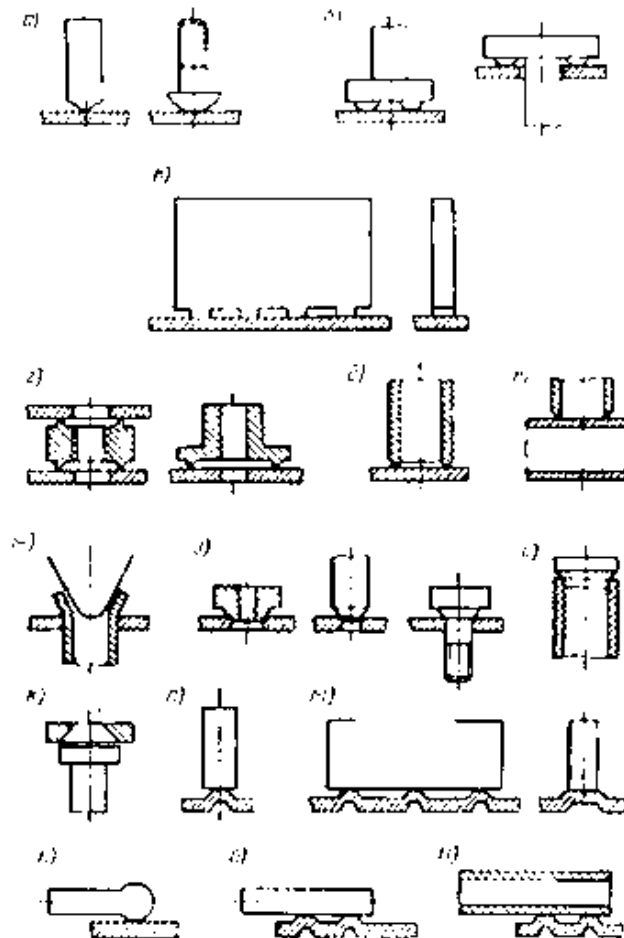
Типы соединений при рельефной тавровой сварке
